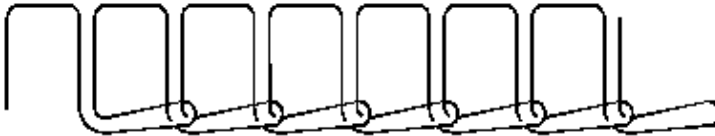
Строение стачивающей однолинейной однониточной строчки цепного стежка
